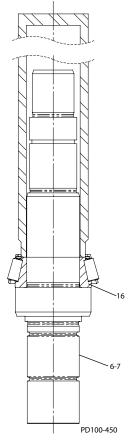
Вставьте внутреннее кольцо конического подшипника в вал
